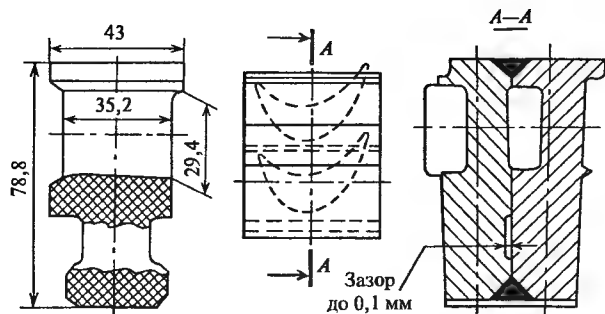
Сварной пакет из двух лопаток ЛМЗ
